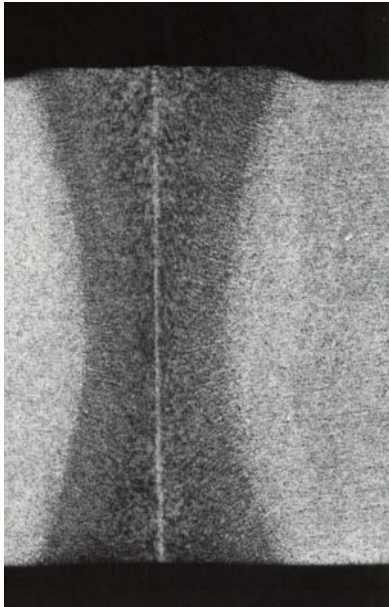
Schliffbild der Schweißnaht für ein HF-geschweißtes Edelstahlrohr [18]
